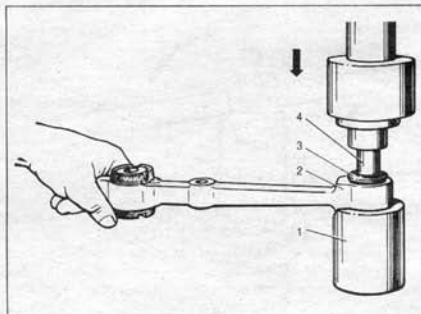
Выпрессовка резинометаллического шарнира из рычага подвески:
